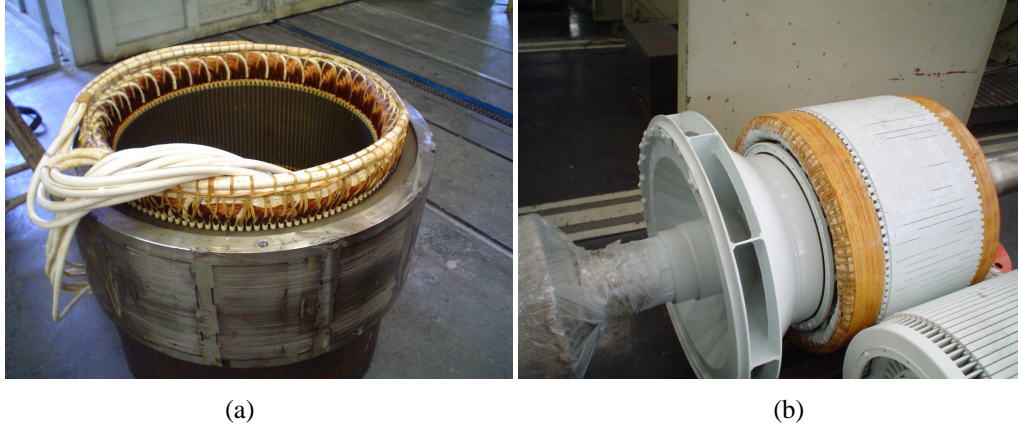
(a) Estator bobinado, (b) Rotor bobinado.
